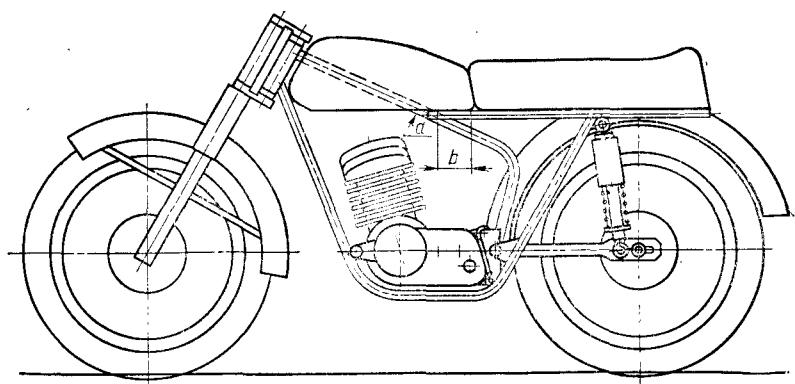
Размещение топливного бака на эскизи компоновке мотоцикла:
